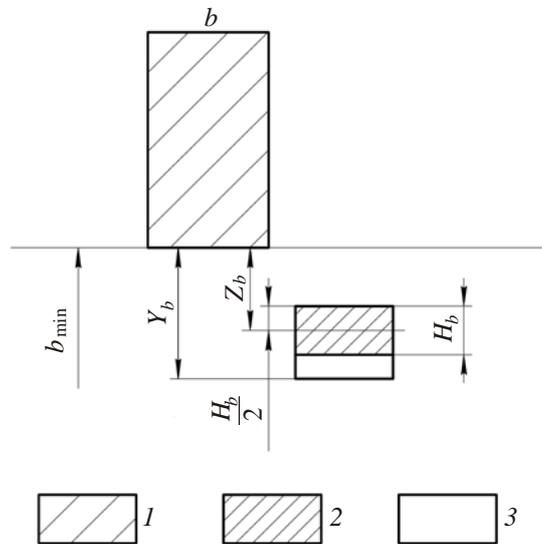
Схема расположения полей допусков калибра-пробки по размеру b :
